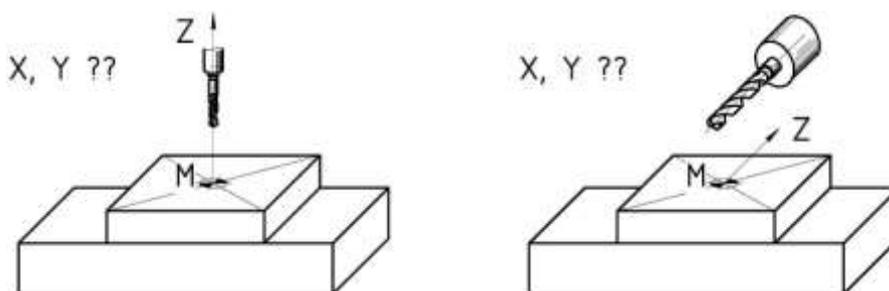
системы координат фрезерных, сверлильных и расточных станков с ЧПУ
